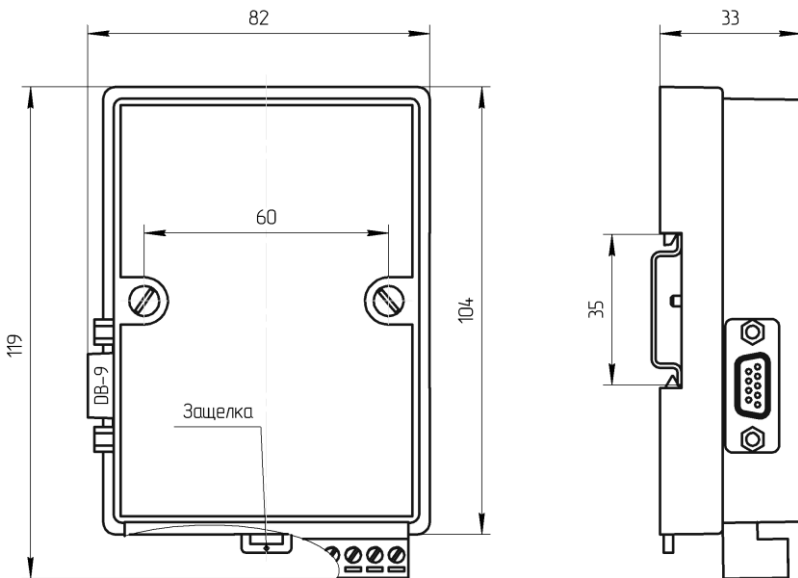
Габаритный чертеж ПЛК с креплением к DIN-рейке
